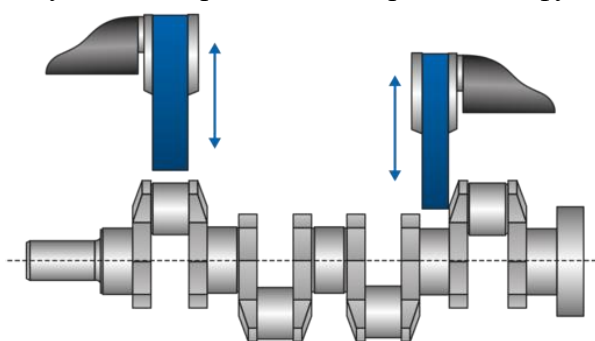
Шліфування колінчастого вала з паралельними осями заготовки та інструмента [11]
